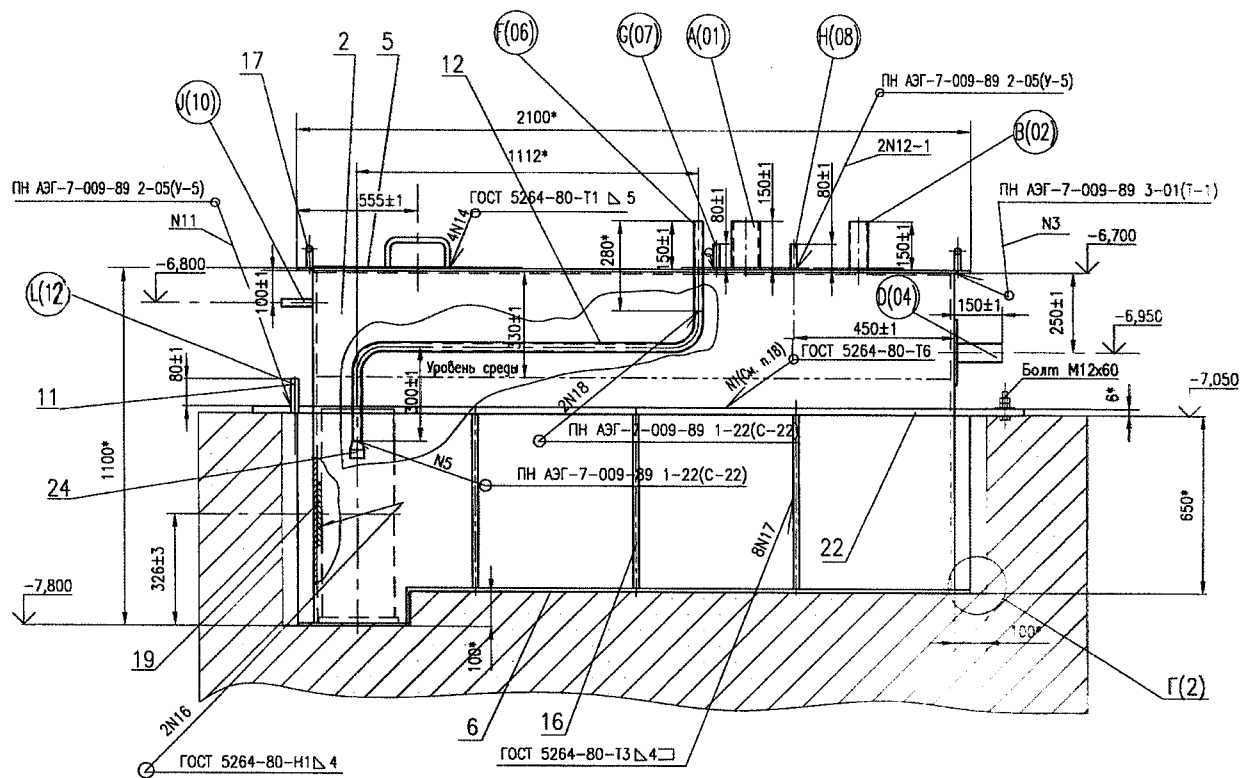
Габаритный чертеж бака сбора боросодержащих дренажей КТА40ВВ001
